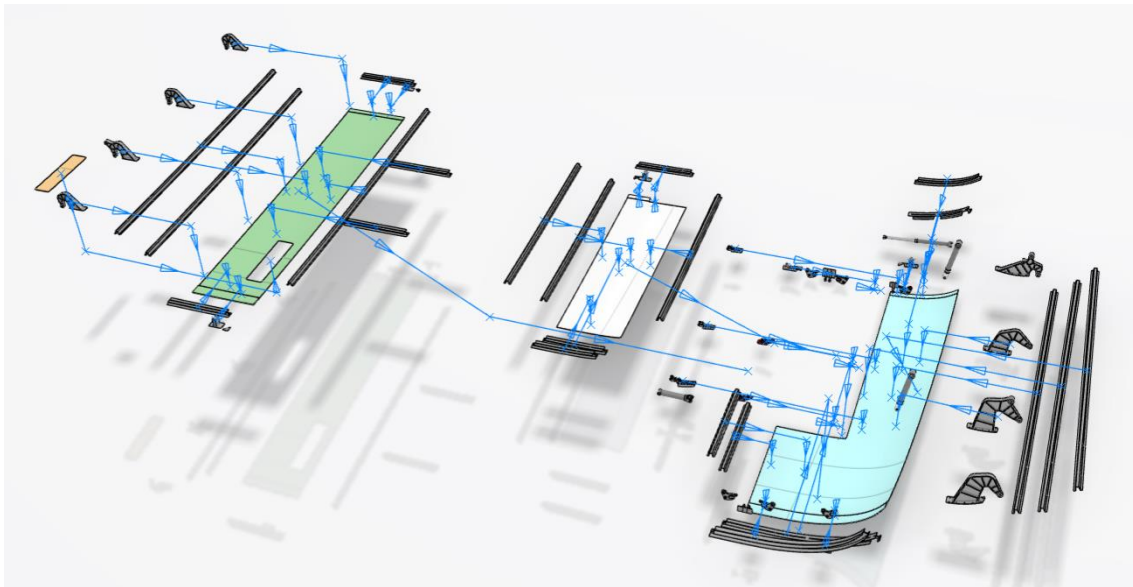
Conjunto de *tracks* para ensamblaje completo
